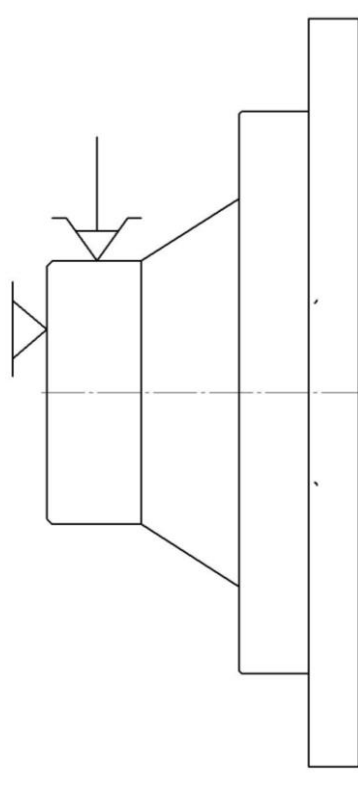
Базування деталі на першій токарній операції з ЧПК
